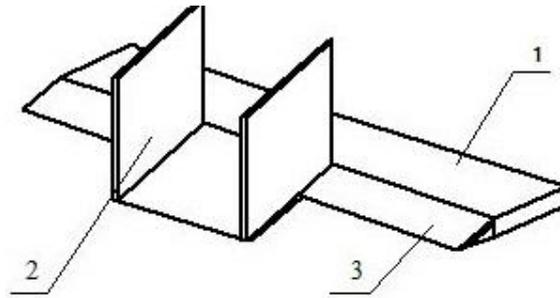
Совковый режущий орган: 1 – днище ковша; 2 – сменный совковый орган; 3 – подножевая плита
